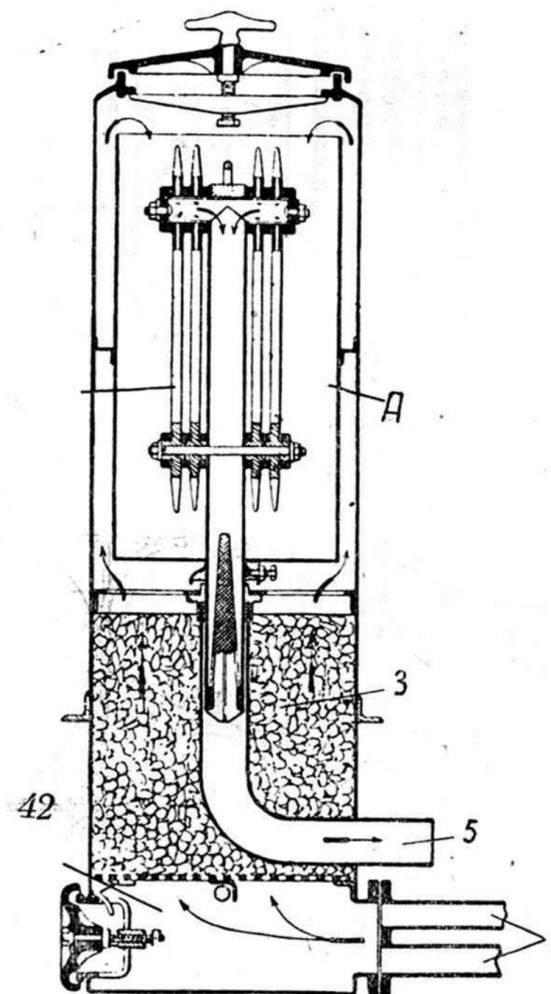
Комбинированный поверхностный очиститель Панар-Левассор. 1 — вход газа; 2 — приемник газа и резервуар для сбора грязи; 3 — слой кокса; 4 — фланельный фильтр; 5 — выход газа
